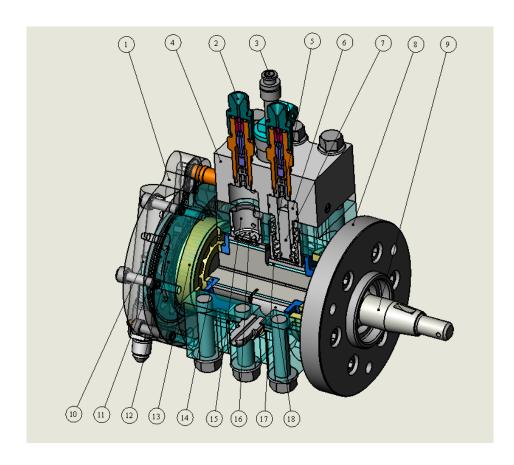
Топливный насос высокого давления для системы Common - Rail: 1-подкачивающий насос, 2-нагнетательный клапан, 3-электромагнитный дозирующий клапан, 4-крышка насоса, 5-пружина, 6-втулка плунжера, 7- плунжер, 8-передняя крышка насоса, 9-эксцетриковый вал, 10-редукционный клапан, 11-наружнее колесо, 12-внутреннее колесо, 13-подшипник, 14-шайба дистанционная, 15-стакан, 16-толкатель, 17-втулка эксцентрикового вала, 18-втулка.
